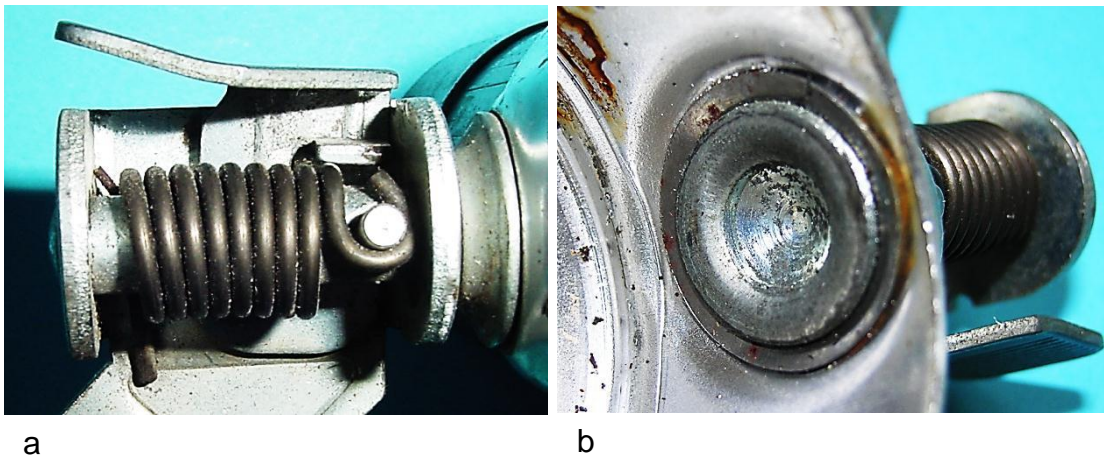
Befestigung des Drehbolzens: a) Flansch am Gehäusemantel, b) Aufweitung der Bohrung des Drehbolzens innerhalb des Gehäuses
